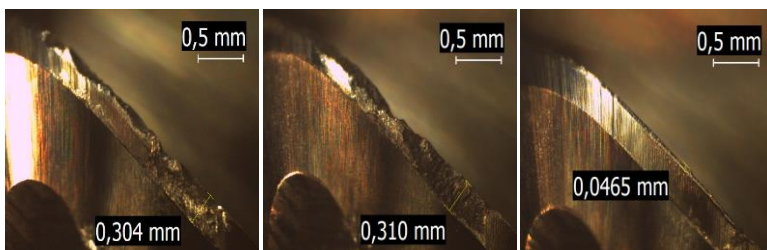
Werkzeugverschleiß an Dichteprobenkörper
